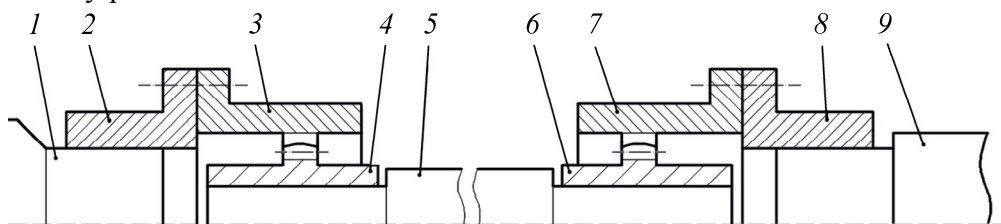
Схема соединения трансмиссионного вала с валом электродвигателя и главным валом вентилятора ВО-21: 1 — вал двигателя; 2, 8 — полумуфта; 3, 7 — обойма; 4, 6 — втулка; 5 — трансмиссионный вал; 9 — главный вал
